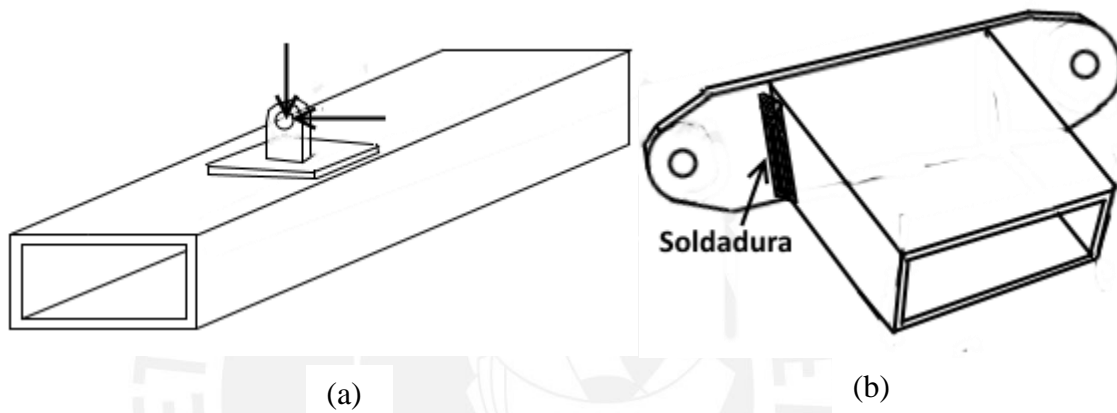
(a) Lugar de aplicación de la fuerza en el actuador (b) Ubicación del cordón de soldadura
